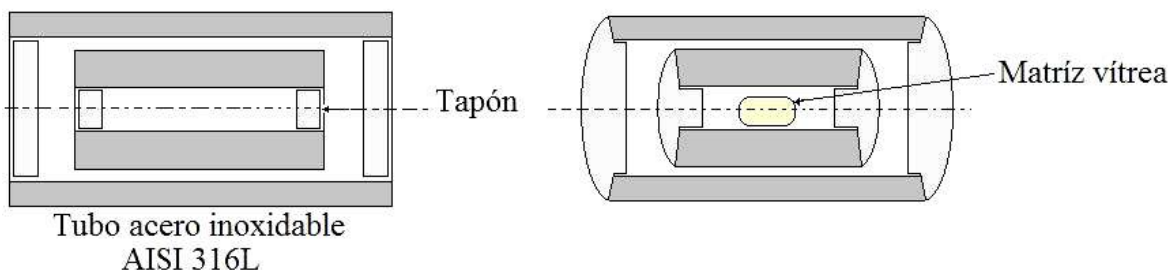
Esquema de cápsulas para ensayo de soldadura. a) Previo; b) Posterior a la soldadura.
